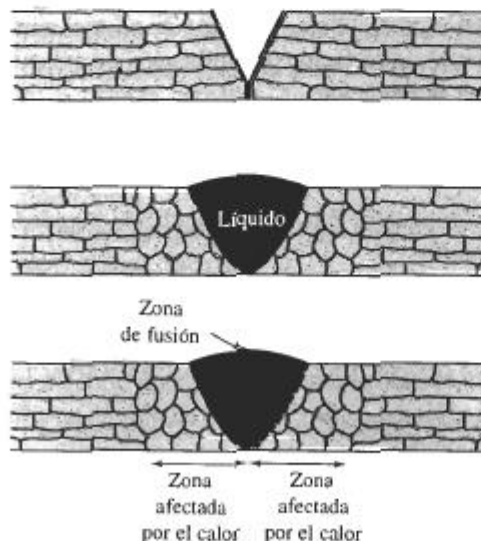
Diagrama esquemático de la zona de fusión y de la solidificación durante la soldadura por fusión: (a) Unión preparada para la soldadura, (b) soldadura a su temperatura máxima, con la unión llena de metal de aporte en estado líquido y (c) soldadura después de la solidificación.
